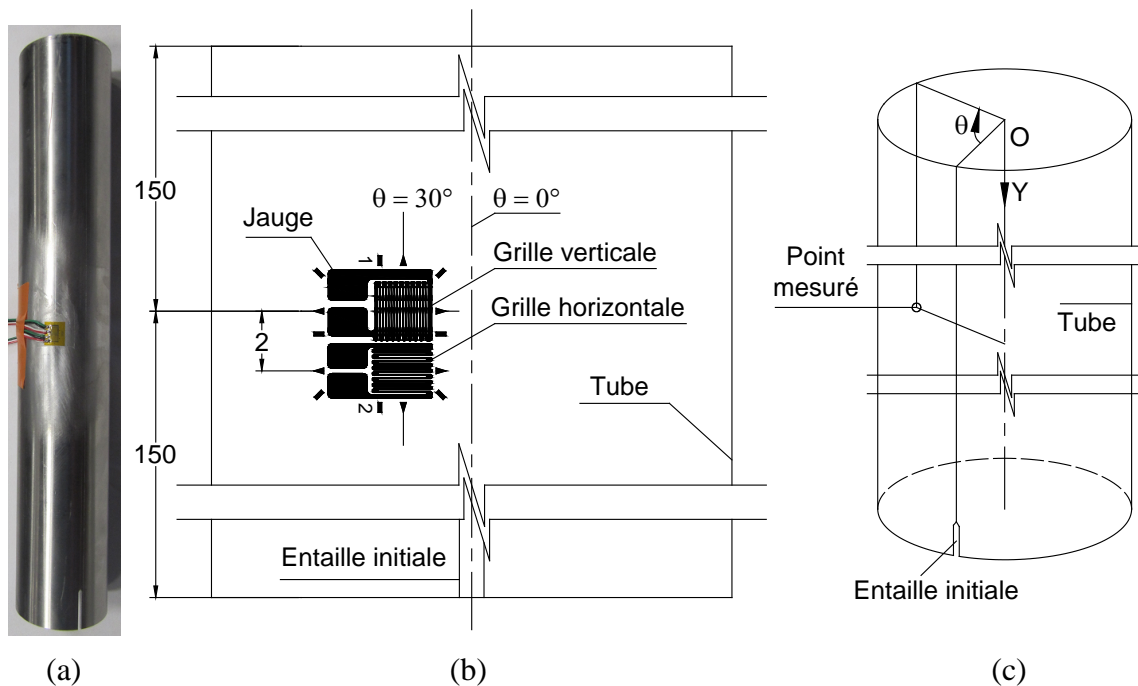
Tube avec jauge, (a) éprouvette, (b) position de la jauge, (c) repère sur tube
